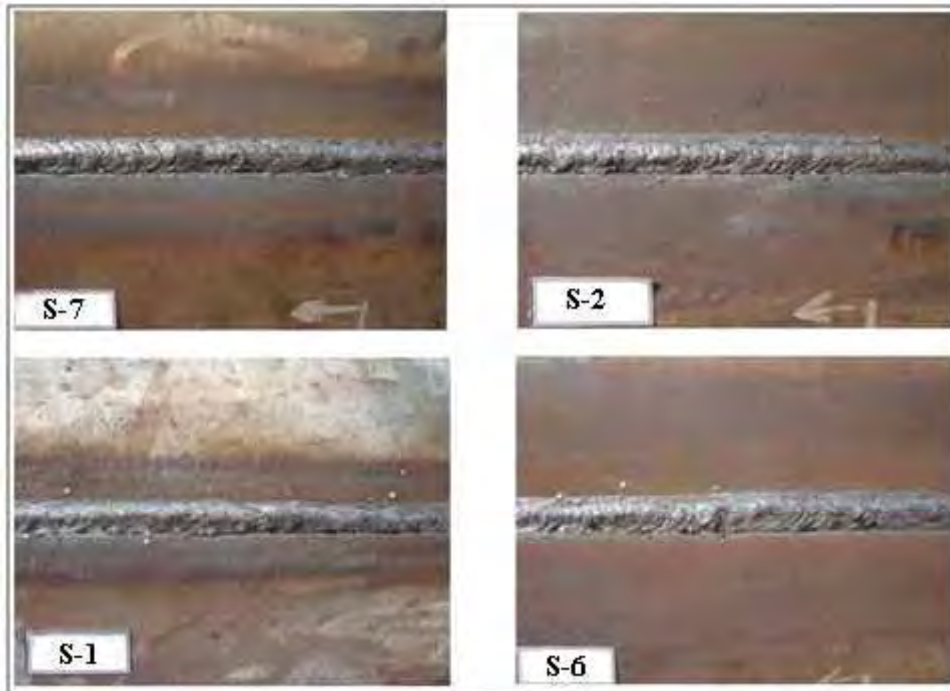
Detalhe visual dos 1ºs cordões das juntas soldadas.
